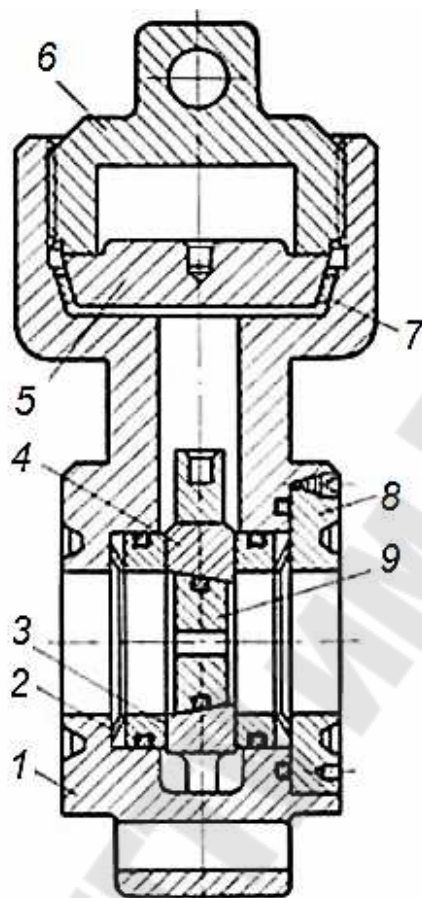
Штуцер быстросменный для фонтанной арматуры высокого давления (ЩБА-50-700): 1 – корпус, 2 – тарельчатая пружина, 3 – боковое седло, 4 – обойма, 5 – крышка, 6 – нажимная гайка, 7 – прокладка, 8 – гайка боковая, 9 – штуцерная металлокерамическая втулка
